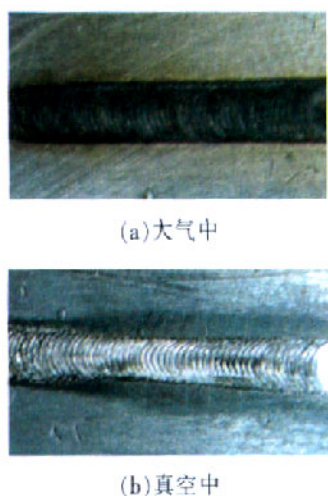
大气和真空环境下304不锈钢焊缝表面形貌
